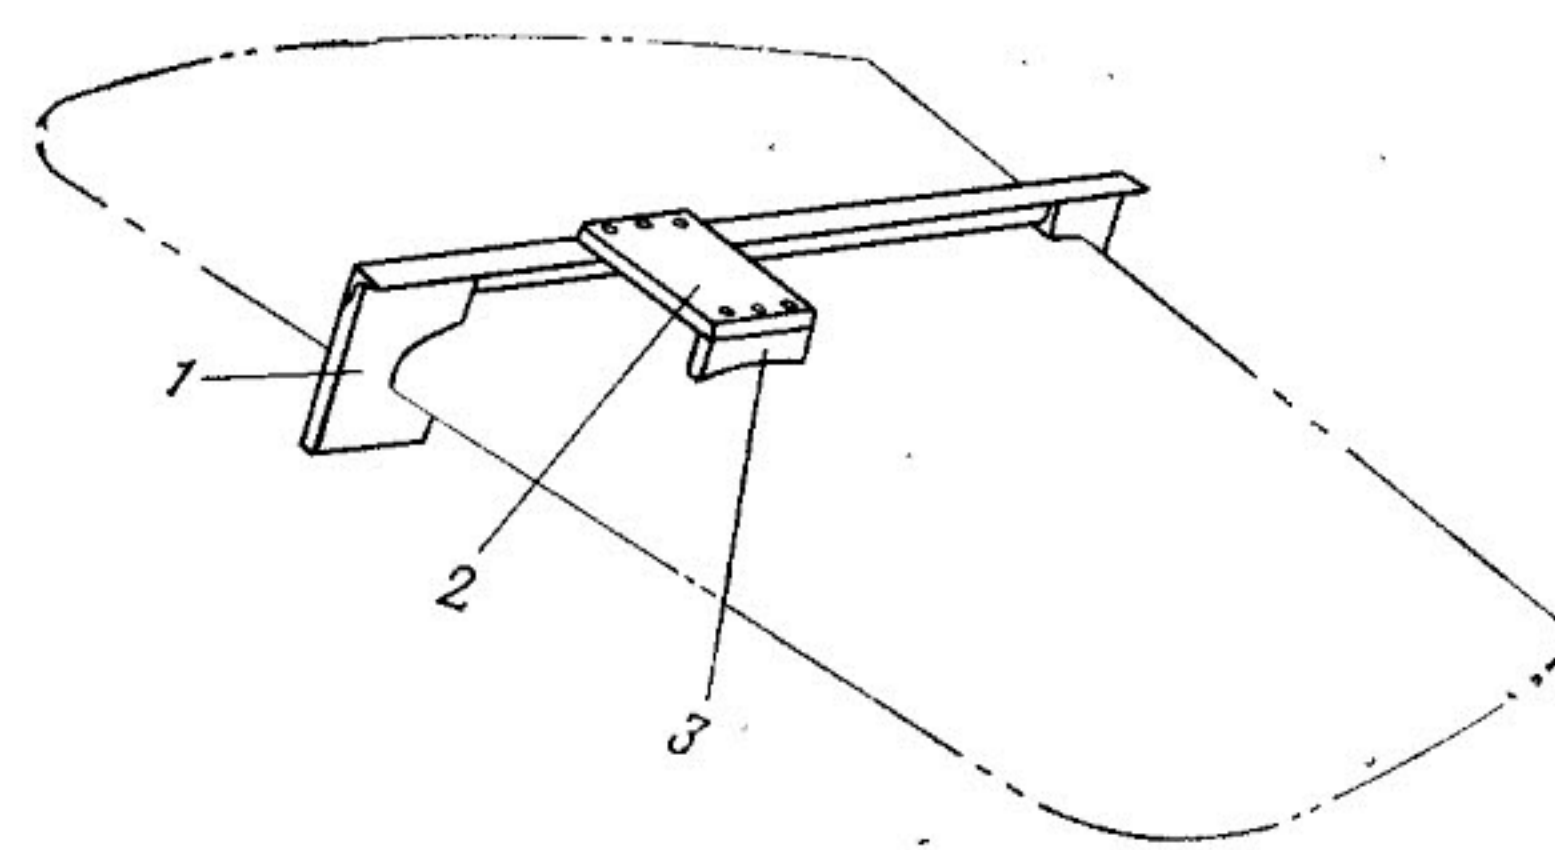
Приспособление для установки угломера на стабилизаторе:
